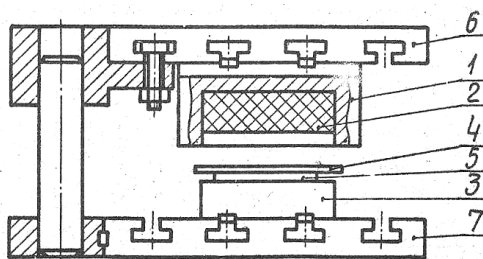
Универсально-сборный штамп для вырубki листовых деталей
